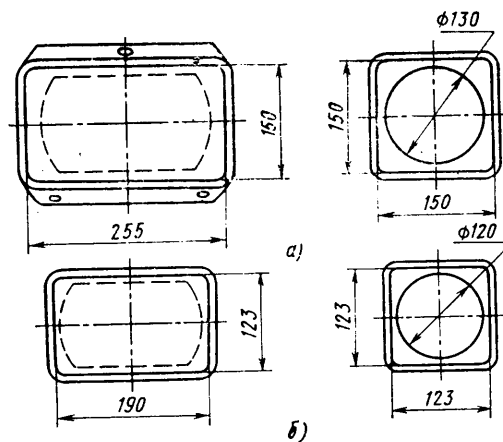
Габаритные размеры и размеры световых отверстий фар двух типоразмерных рядов: а — первый ряд; б — второй ряд
